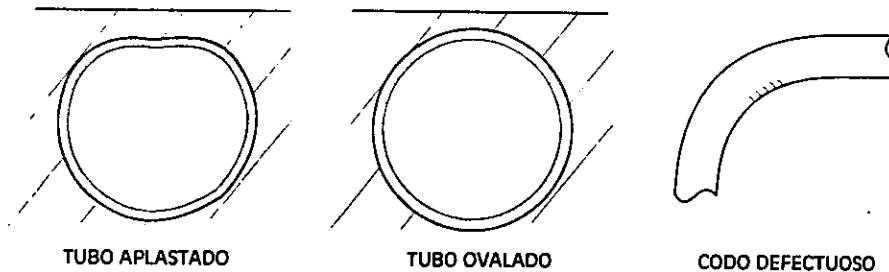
TIPOS DE FALLAS EN TUBERÍAS
